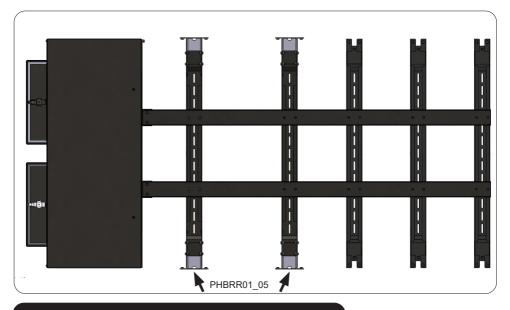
verschraubter Querstreben Halter/ bolted cross strut bracket
